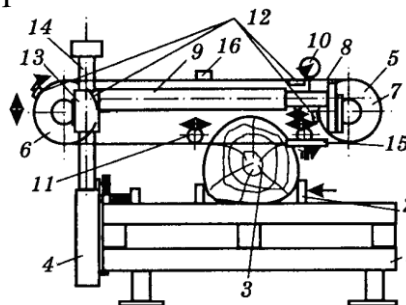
Принципова схема горизонтального стрічкопилкового верстата: 1 – станина; 2 – затискач колоди; 3 – колода; 4 – каретка; 5 – стрічкопилковий супорт; 6, 7 – приводний і натяжний шківи; 8 – пилка стрічкова; 9 – пристрій для натягу пилки; 10 – манометр; 11 – напрямні пилки; 12 – щітка; 13 – гільза; 14 – стійка; 15 – окорювачі; 16 – плоска напрямна
